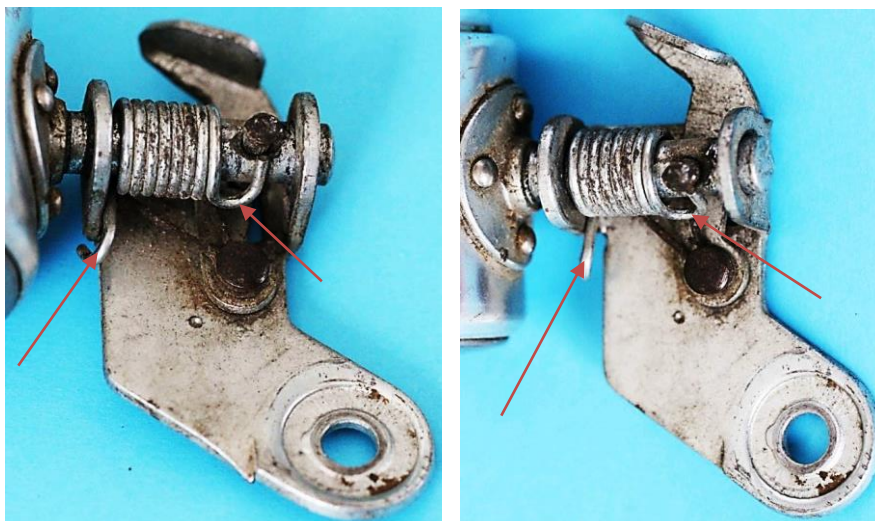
Basisblech mit ausgehängter Druckfeder
